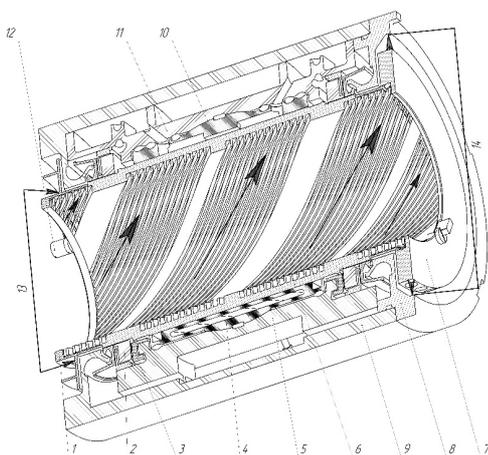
Конструкция автономного подшипника для электродвигателя $\varnothing 115$ - $\varnothing 180$ мм:
